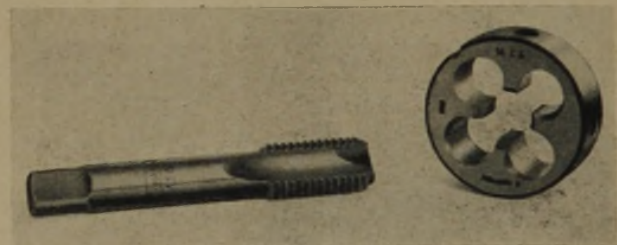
Gewindebohrer und Schneideisen mit Schälanschnitt
